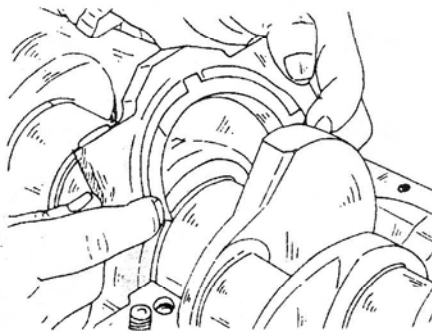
Установка крышки коренного подшипника с регулировочной шайбой.
